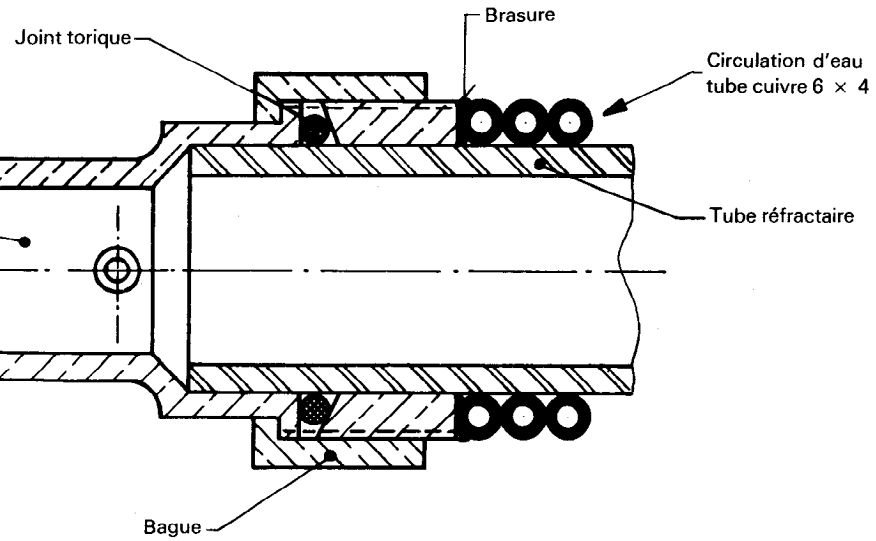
Tête métallique réfrigérée pour tube à combustion
